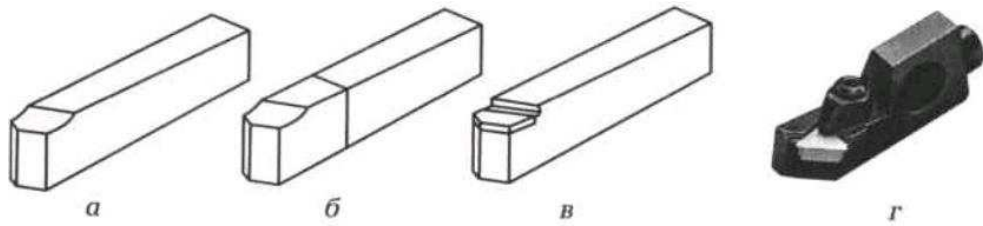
Типы резцов, определяемые по способу крепления их режущей части:
